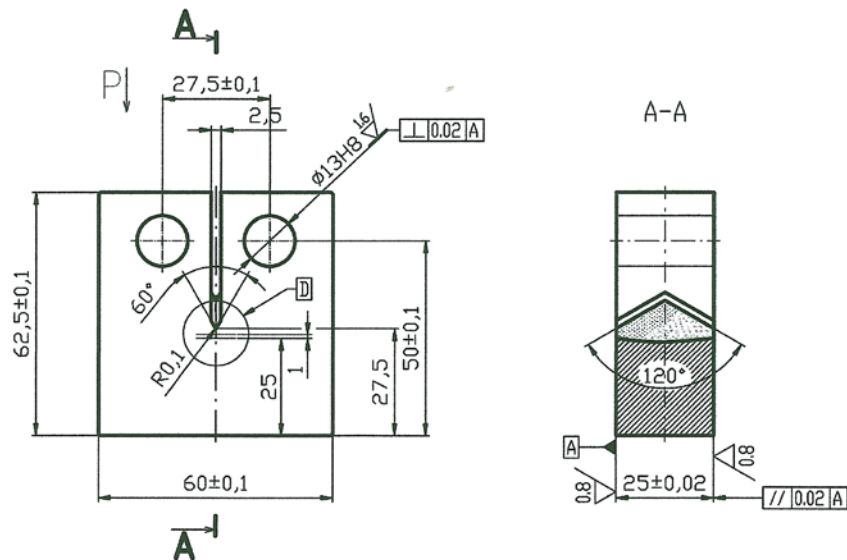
Geometrie zkušebních těles pro zkoušku tahem
